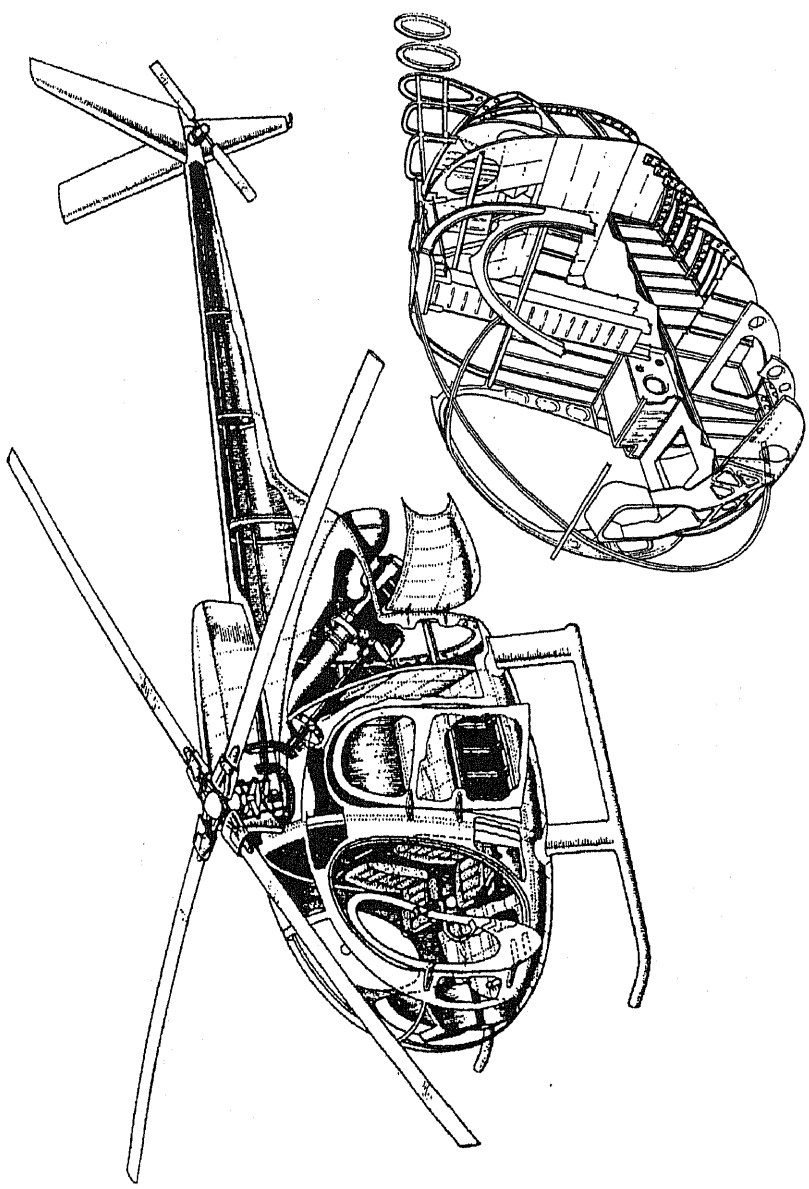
Конструкция фюзеляжа вертолета MD-500
